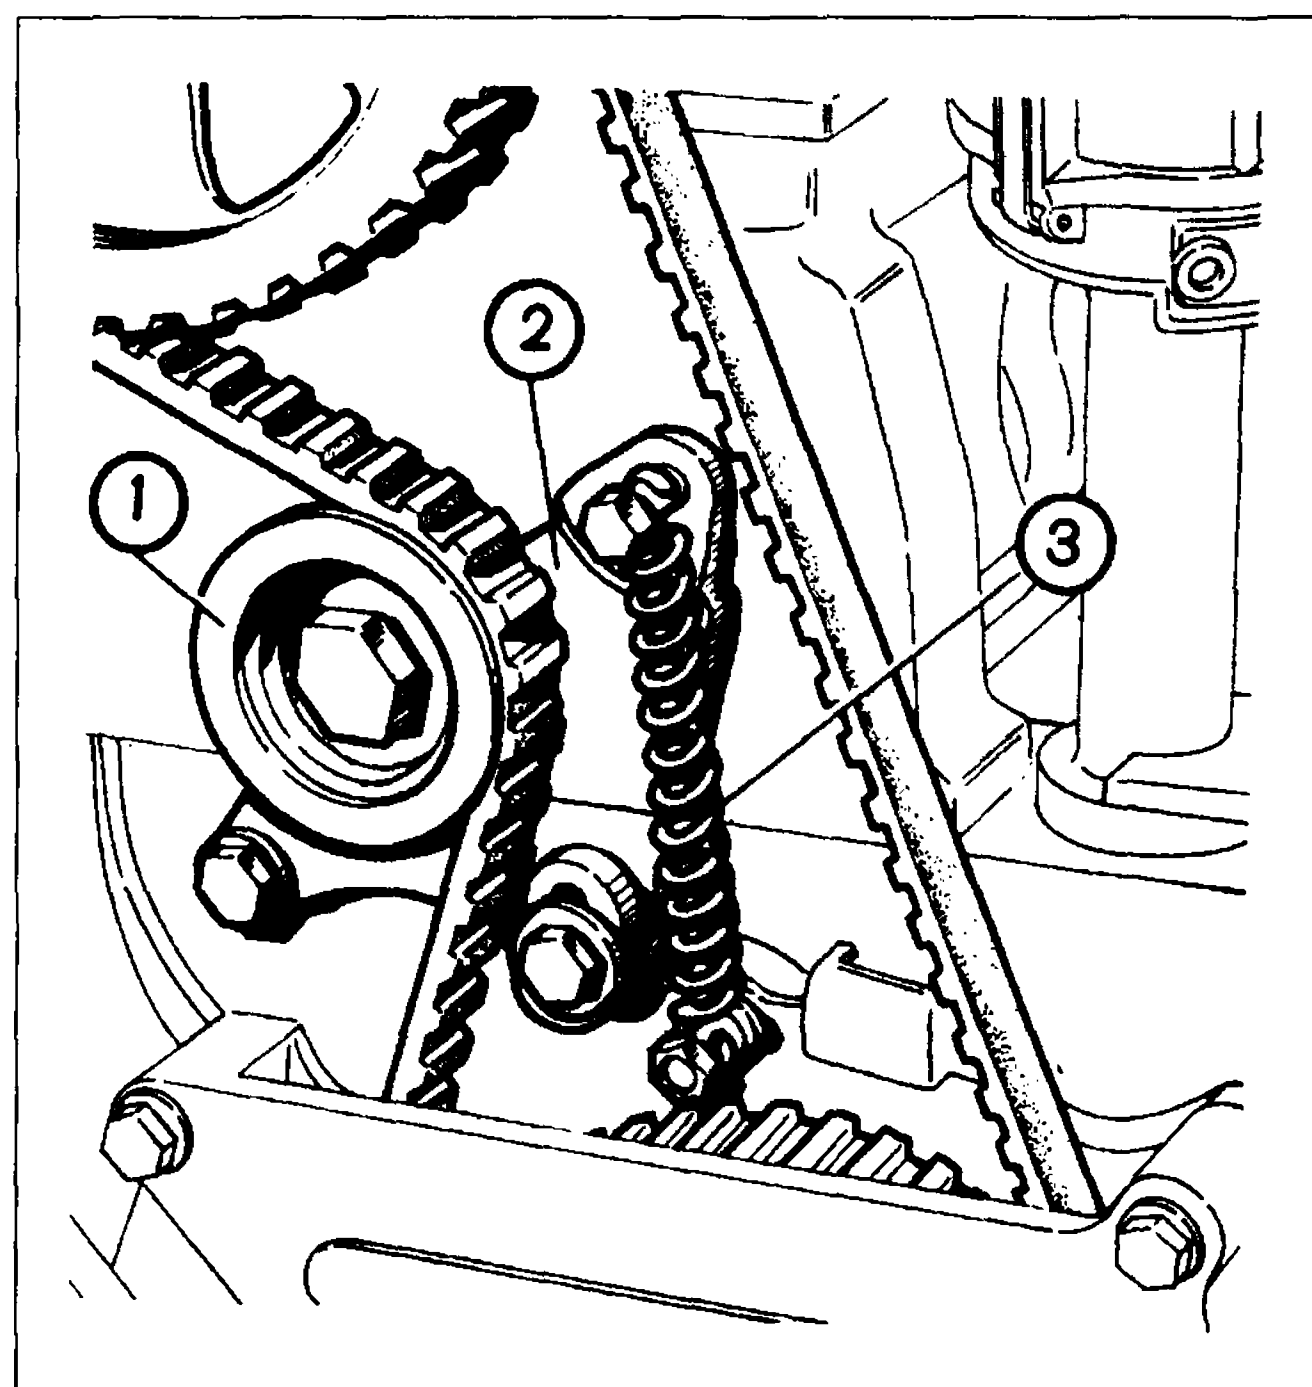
Механизм натяжения ремня привода распределительного вала:
